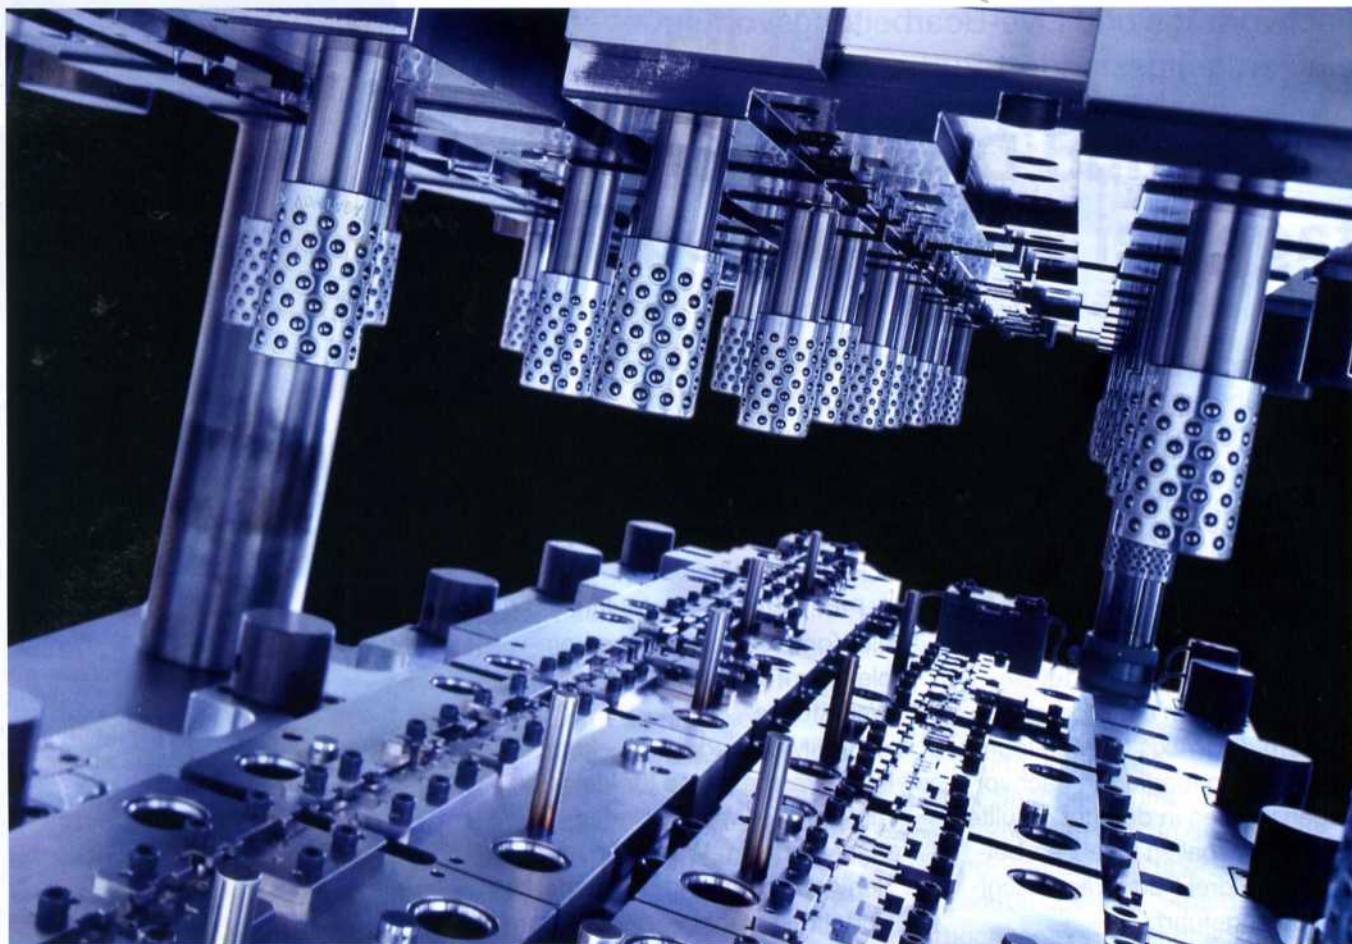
Schroeder+Bauer fertigt mit höchster Präzision und Zuverlässigkeit Umformwerkzeuge für Crimp- und Einpresskontakte
